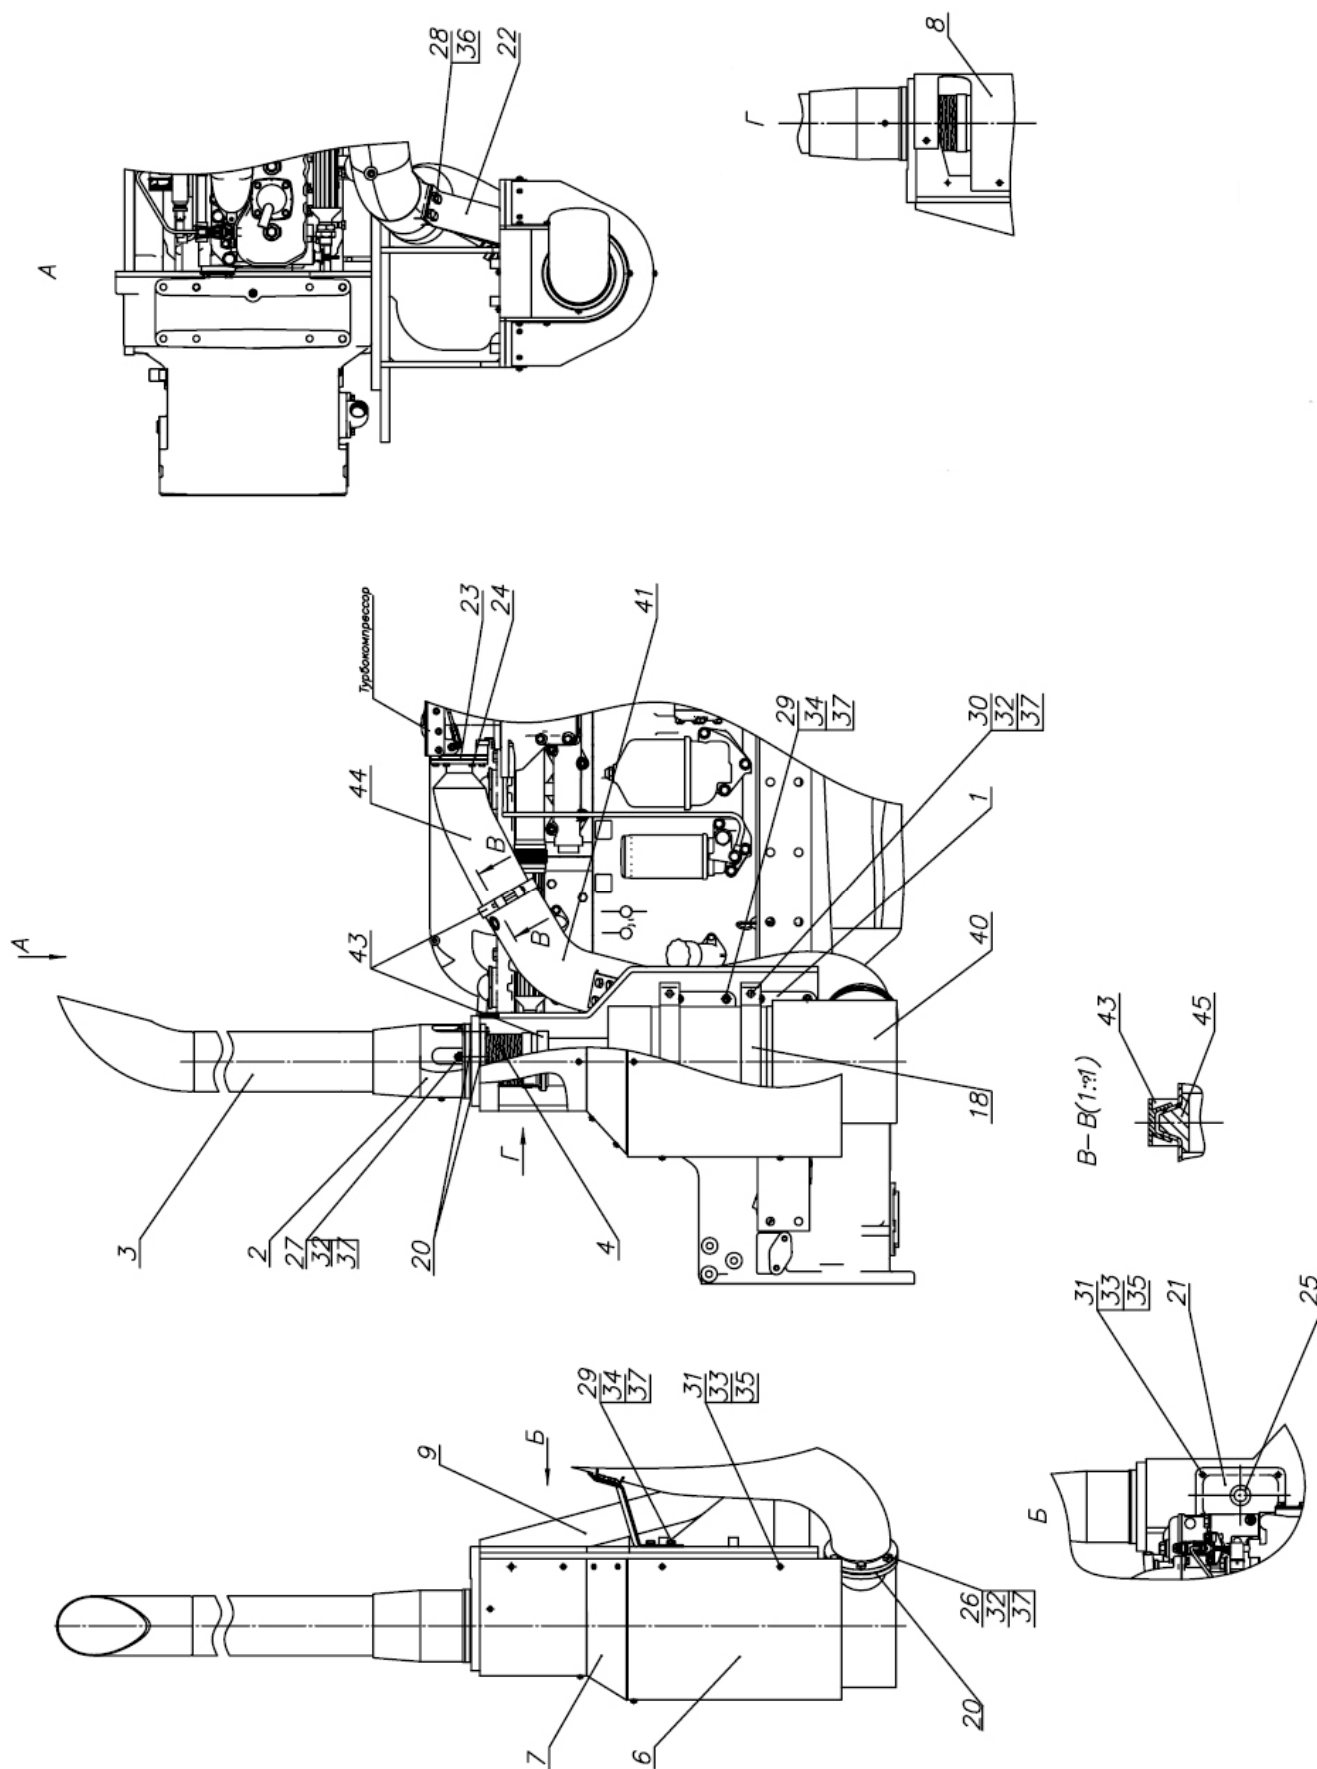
Установка глушителя 2022.5P-1205005-01
